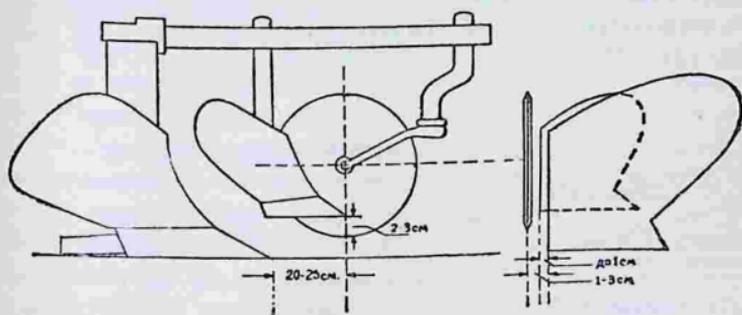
Взаиморасположение главного корпуса, ножа и предплужника. Размеры показаны в см
